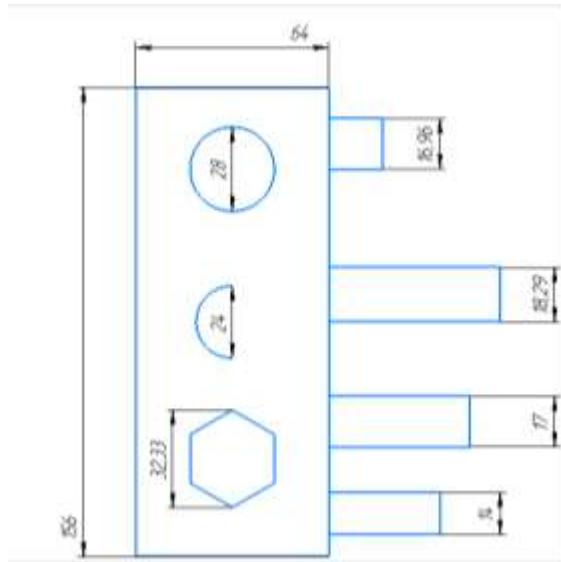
Простановка размеров с использованием инструмента «Авто-размер»
